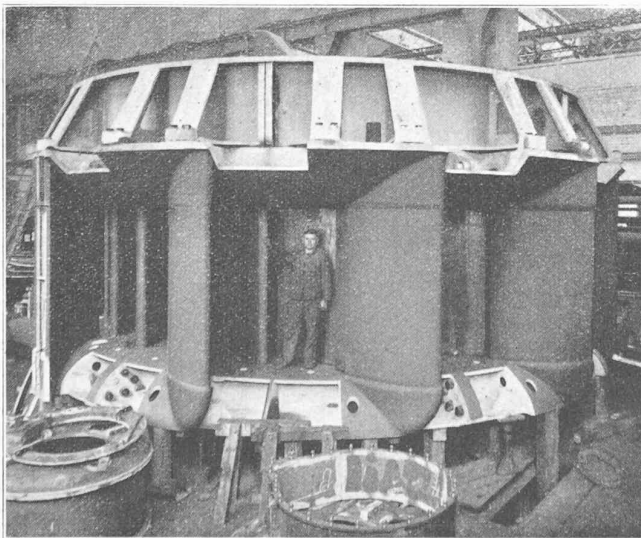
Vue d'une des turbines pendant son montage en atelier.
